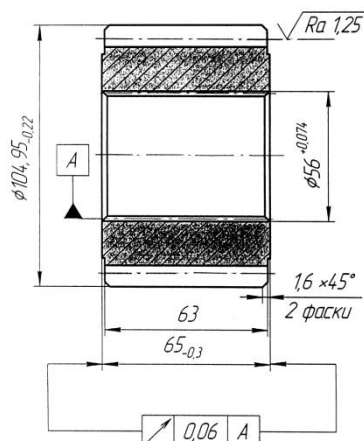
Ведущая цилиндрическая шестерня планетарной передачи
